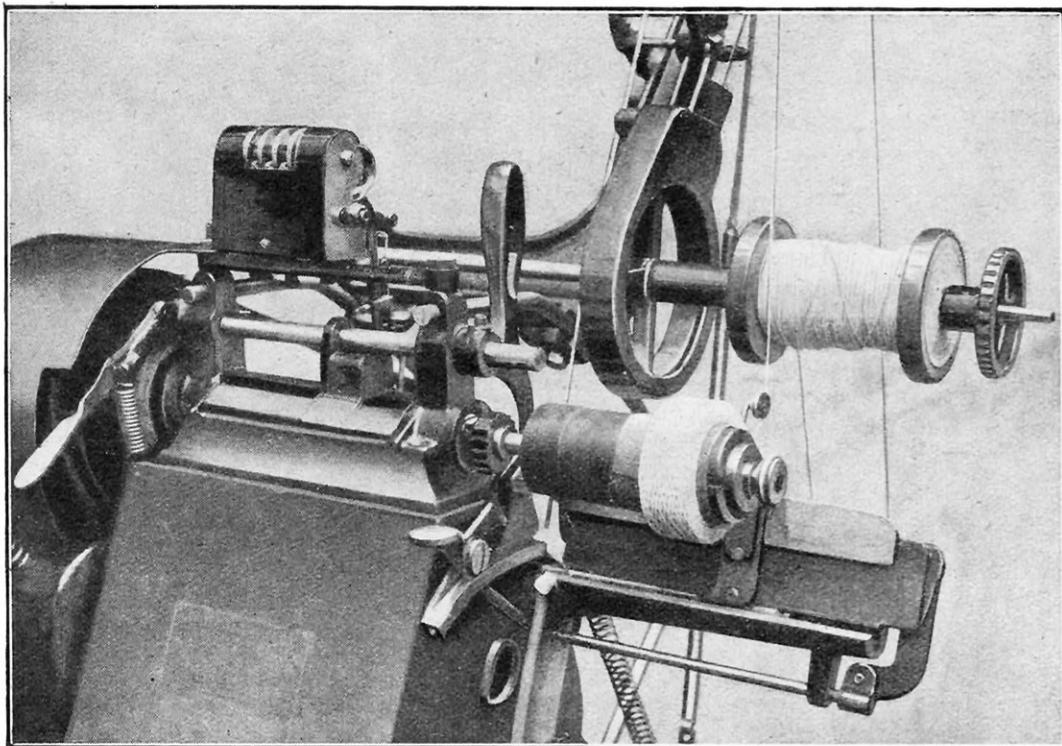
DÉTAILS DU MÉCANISME DE LA MACHINE A FABRIQUER LES BOBINES « NID D'ABEILLE »
